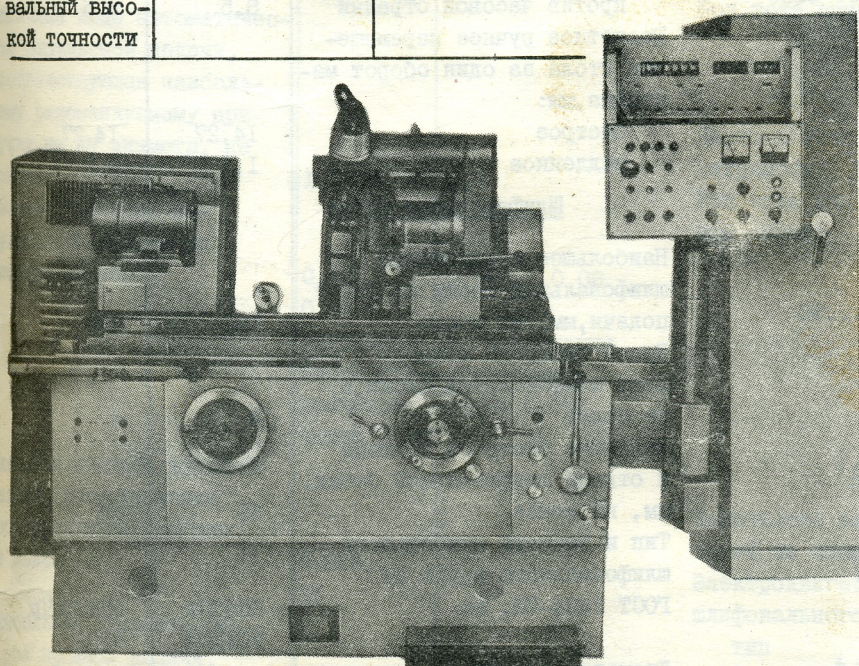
Станок универсальный круглошлифовальный ЗУ12УВФ10
